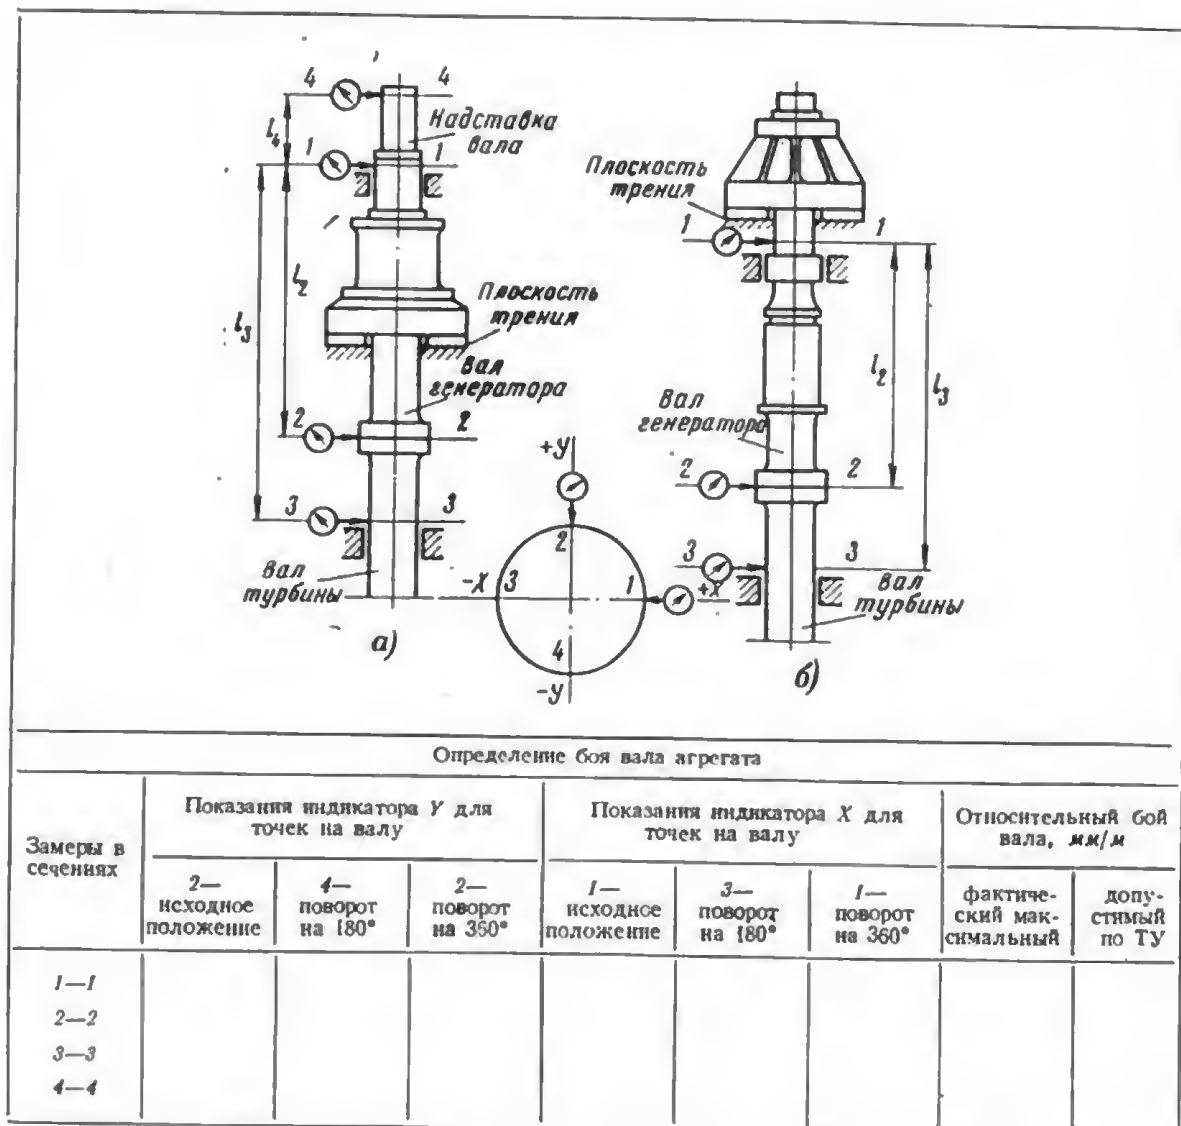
Формуляр проверки оси вала гидроагрегата с поворотом на 180°. а — гидроагрегат с генератором зонтичного типа; б — гидроагрегат с генератором подвесного типа.
